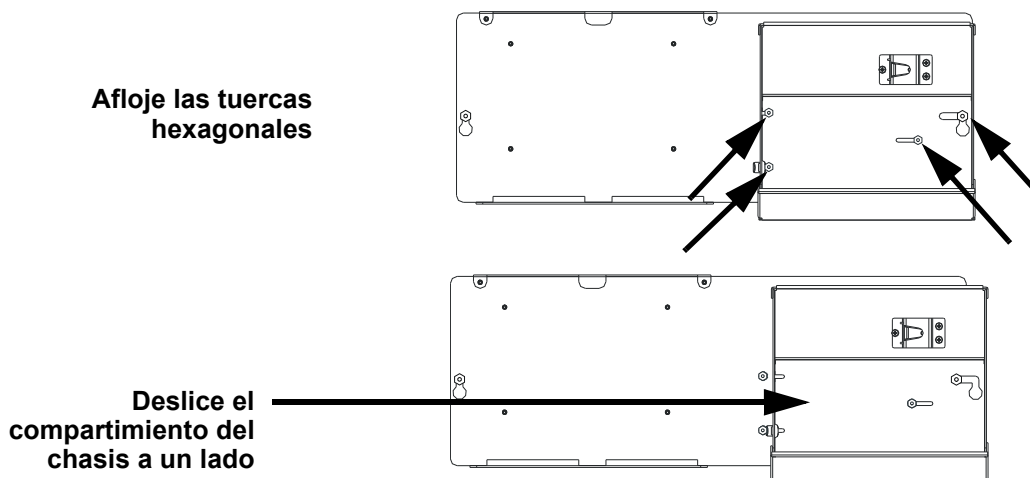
Hacer a un lado el chasis CMIC-1 para acceder al cableado
